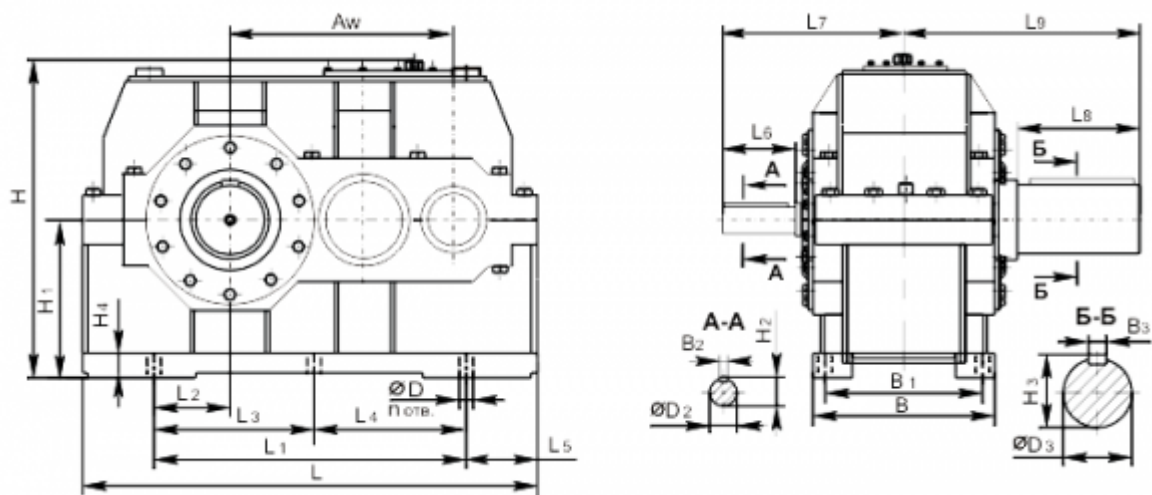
Редуктор циліндричний двоступеневий Ц2-1250
